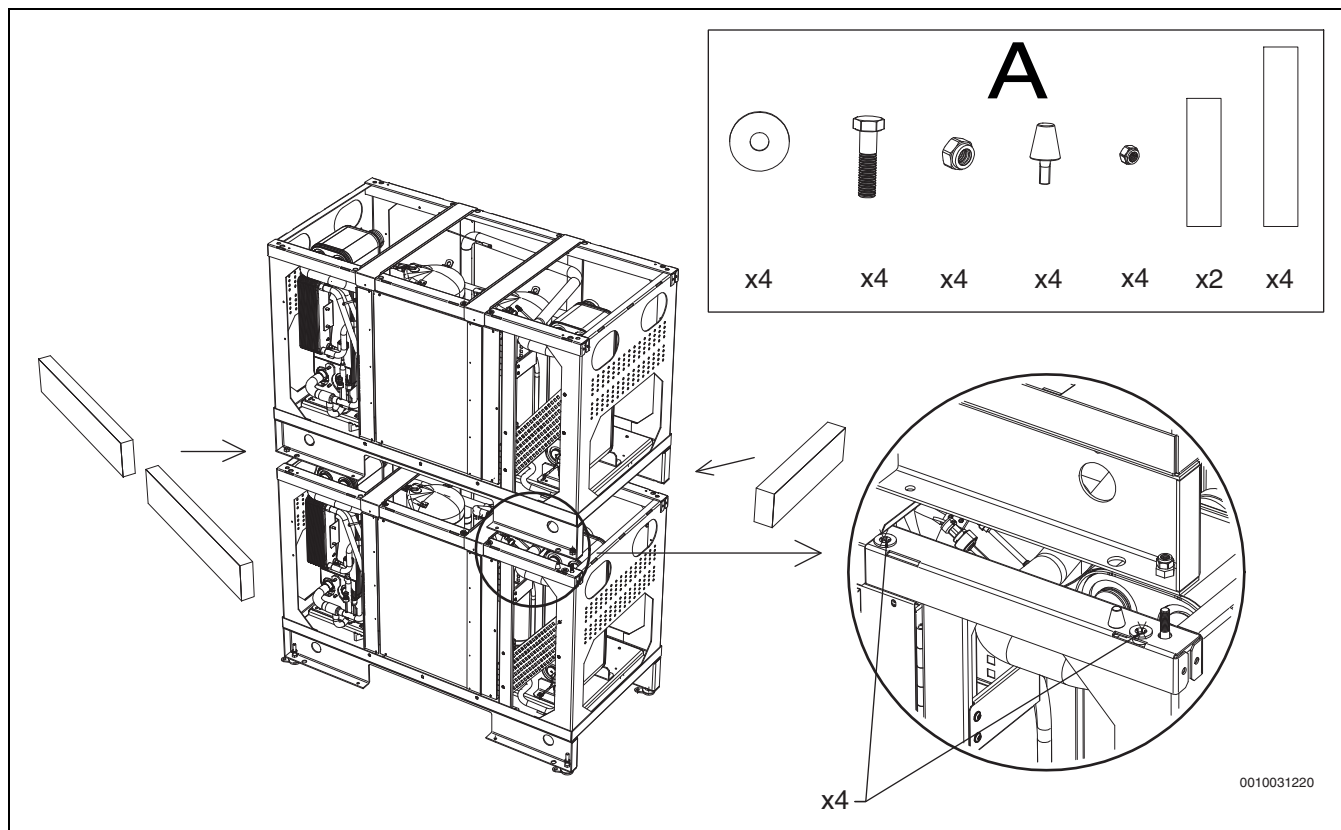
Alternativa pro přepravu tepelného čerpadla 54-80 kW
